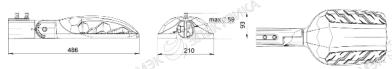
Общий вид светильника Street 9M с консольным поворотным креплением.
